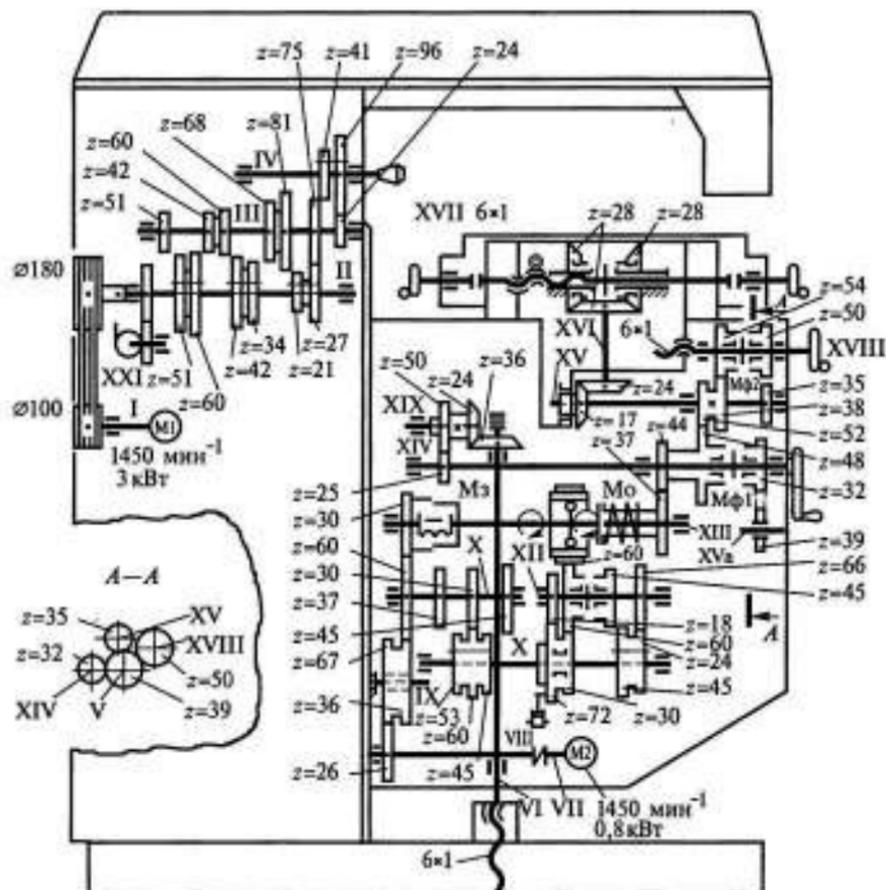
Кинематическая схема универсального консольно-фрезерного станка
